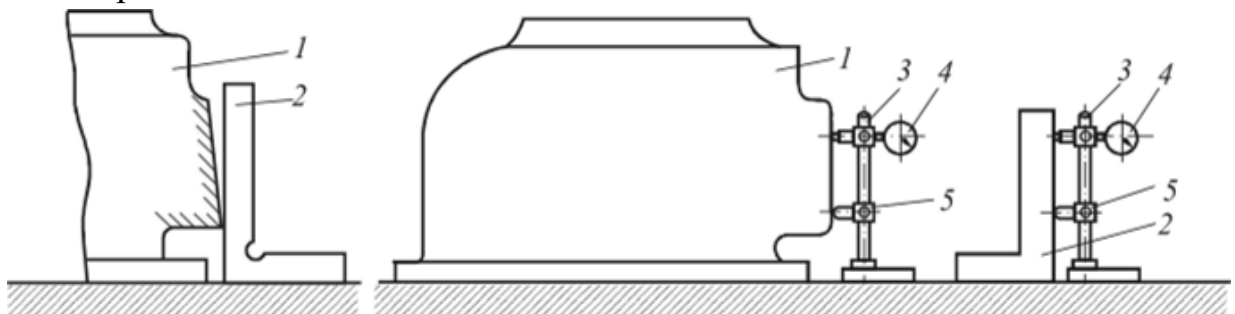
Схема вимірювання відхилень від перпендикулярності площин корпусної деталі
